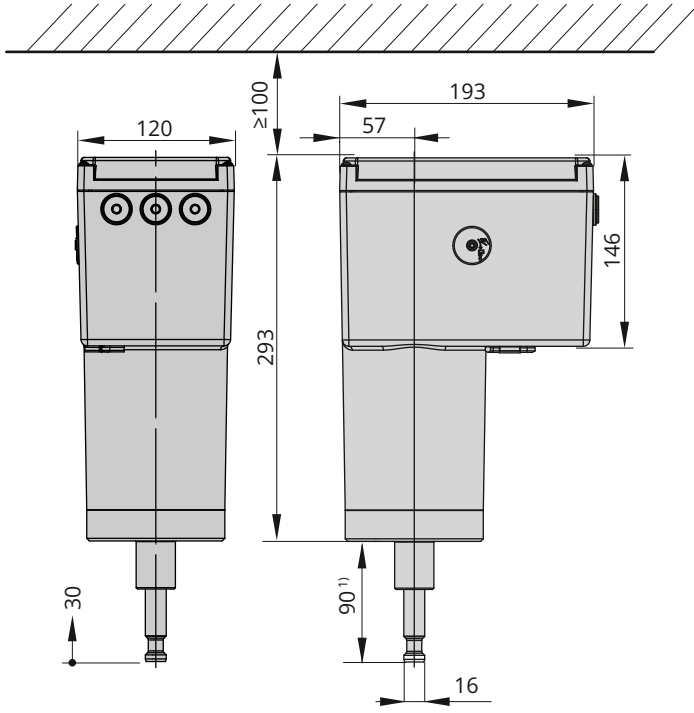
mm cinsinden boyutlar · Tip 3374-25 ve -27, form A versiyonu
